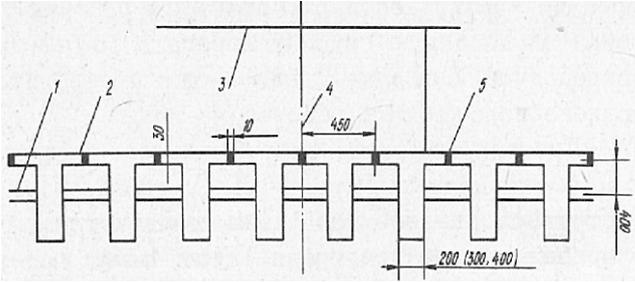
Разметка для проверки и установки рабочих органов навесного культиватора:
